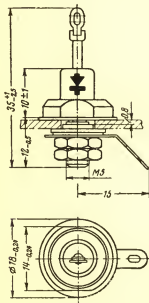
Габаритный чертеж диодов Д227А—Д227И.
